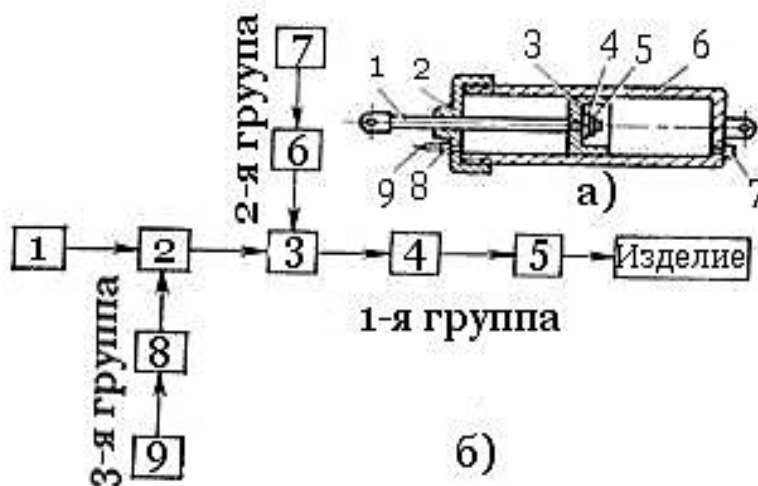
Силовой цилиндр и схема его сборки по базовой детали:
